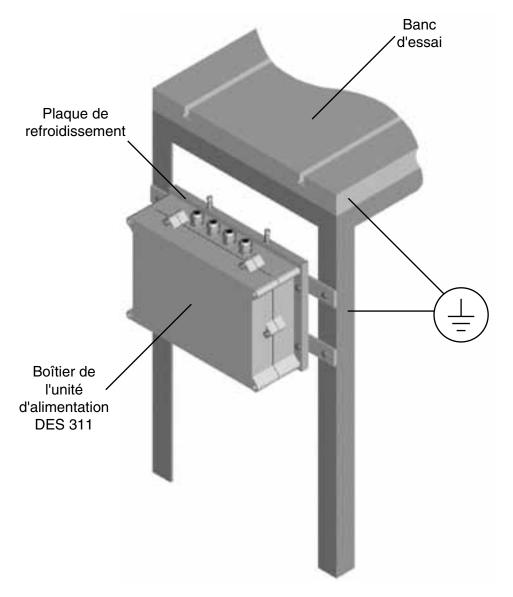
Exemple de montage du DES 311 fixé sur une plaque de refroidissement à eau
